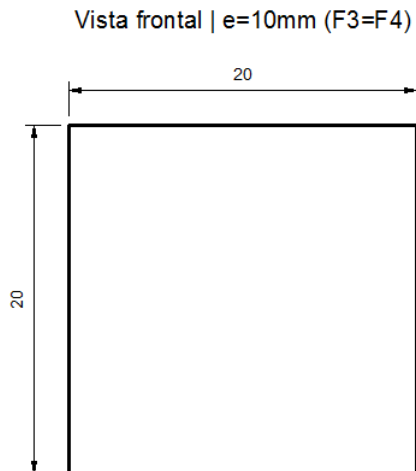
Detalhe das faces F3 e F4, dimensões em cm.
